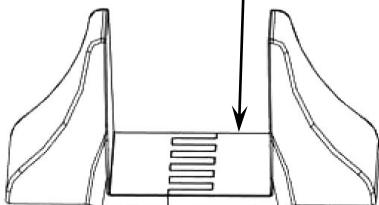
Сборка пластиковых основ для вертикальной установки изделия.
